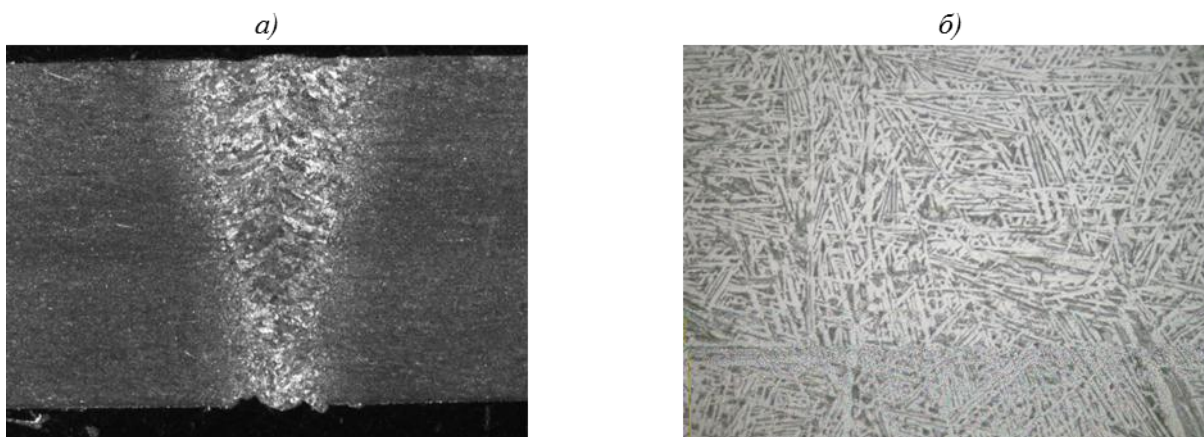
Структура сварного соединения плит из сплава ВТ18У, выполненного ЭЛС, после отжига при 950°С
